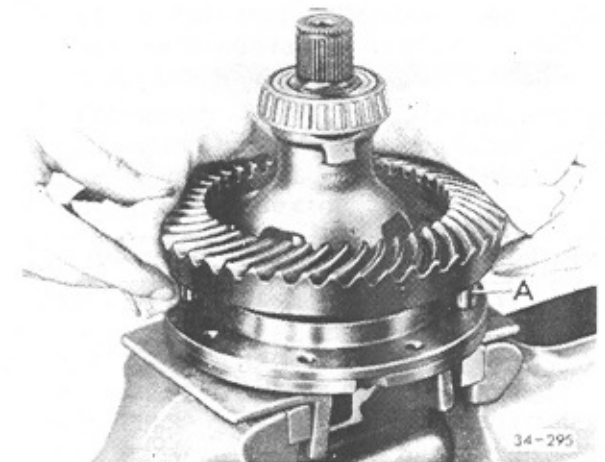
Tellerrad auf ca. 100° C erwärmen und aufsetzen
